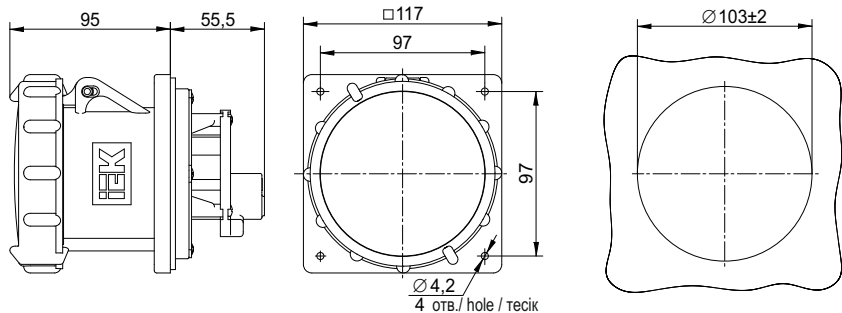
Габаритные размеры соединителей типа ССИ-433, ССИ-434, ССИ-435 / Figure 12 – Overall dimensions of plug and socket-outlets SSI-433, SSI-434, SSI-435 / Сурет 12 – ССИ-433, ССИ-434, ССИ-435 типті жалғастырғыштардың габариттік өлшемдері
